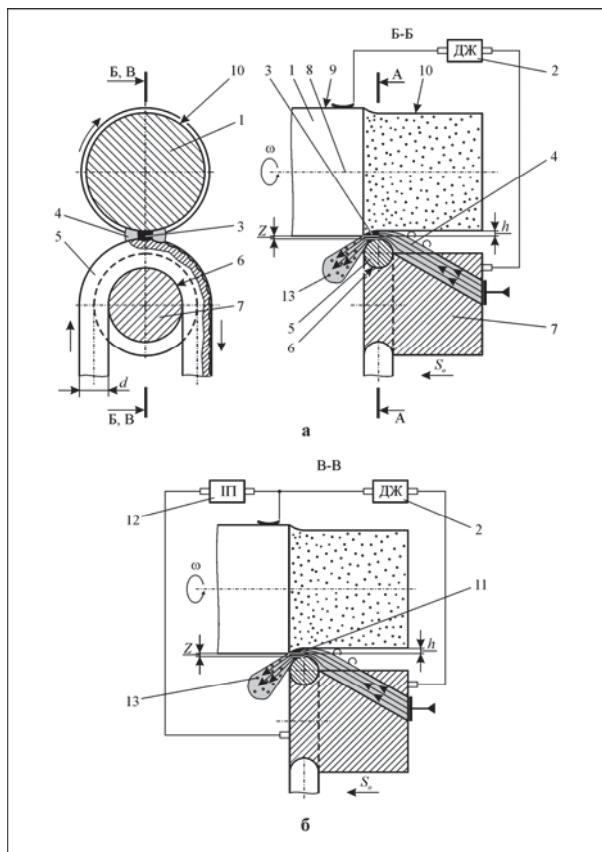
Технологічна схема формоутворення поверхні тіла обертання, що пропонується
